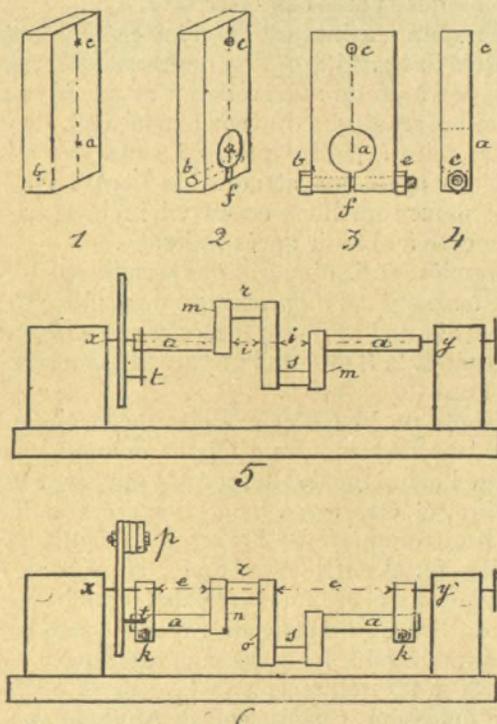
Montage d'un arbre manivelle pour son usinage sur le tour.
